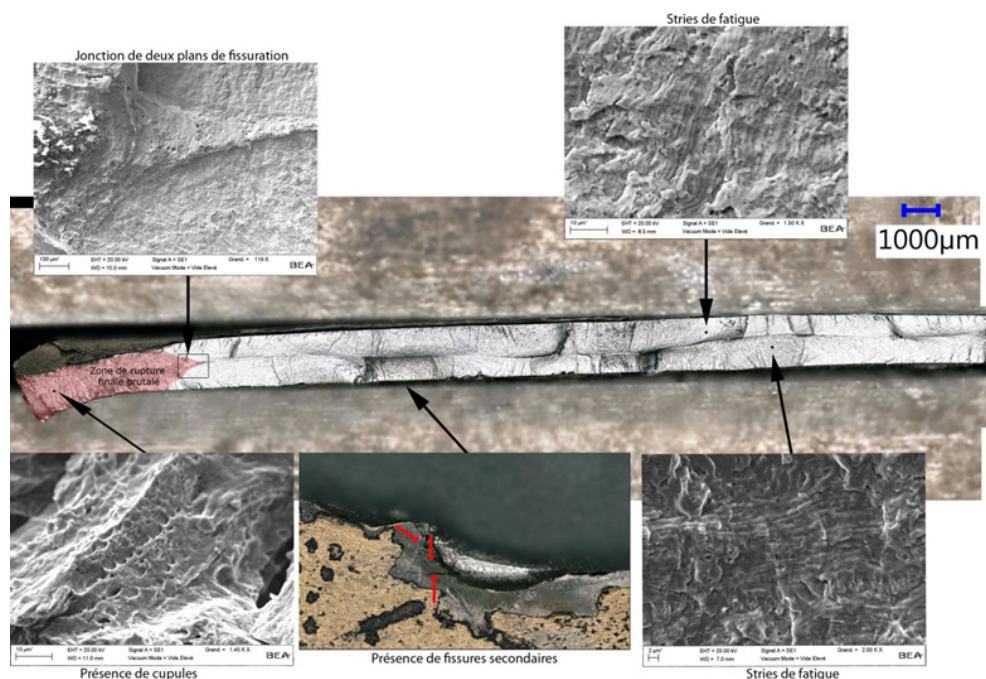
examen fractographique du faciès de rupture de la fixation gauche
